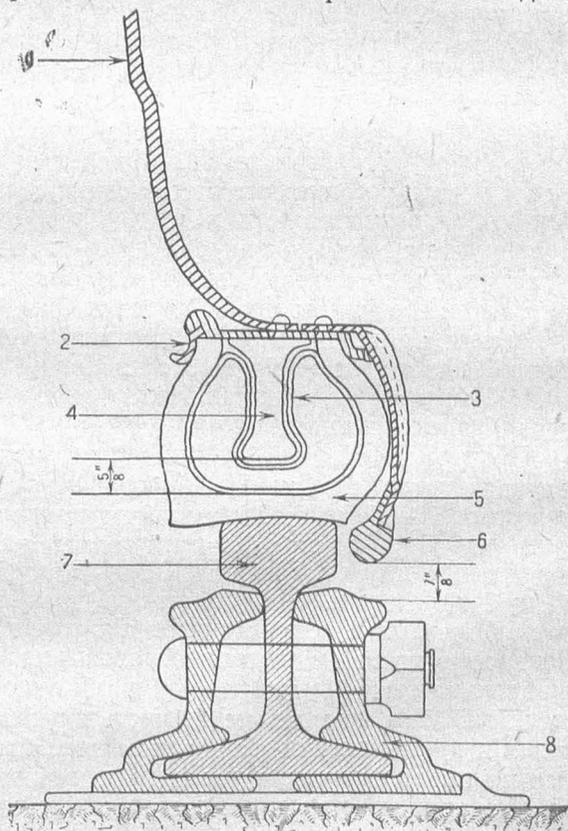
Колесо железнодорожного вагона; 1 — стальное колесо; 2 — запорное кольцо; 3 — внутренняя трубка; 4 — алюминиевое кольцо; 5 — резиновый башмак; 6 — стальной борт; 7 — стальной рельс; 8 — накладка
